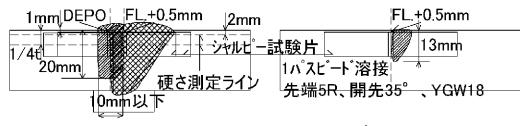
補修溶接の衝撃試験採取位置及び硬さ試験位置
